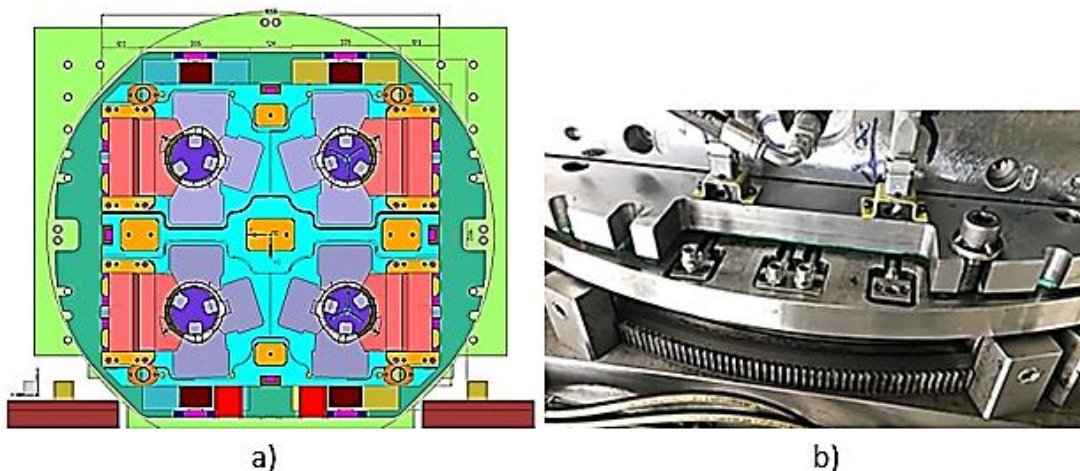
a) Fixação do molde por parafusos, em projeto; b) Fixação do molde por parafusos, em ensaio
